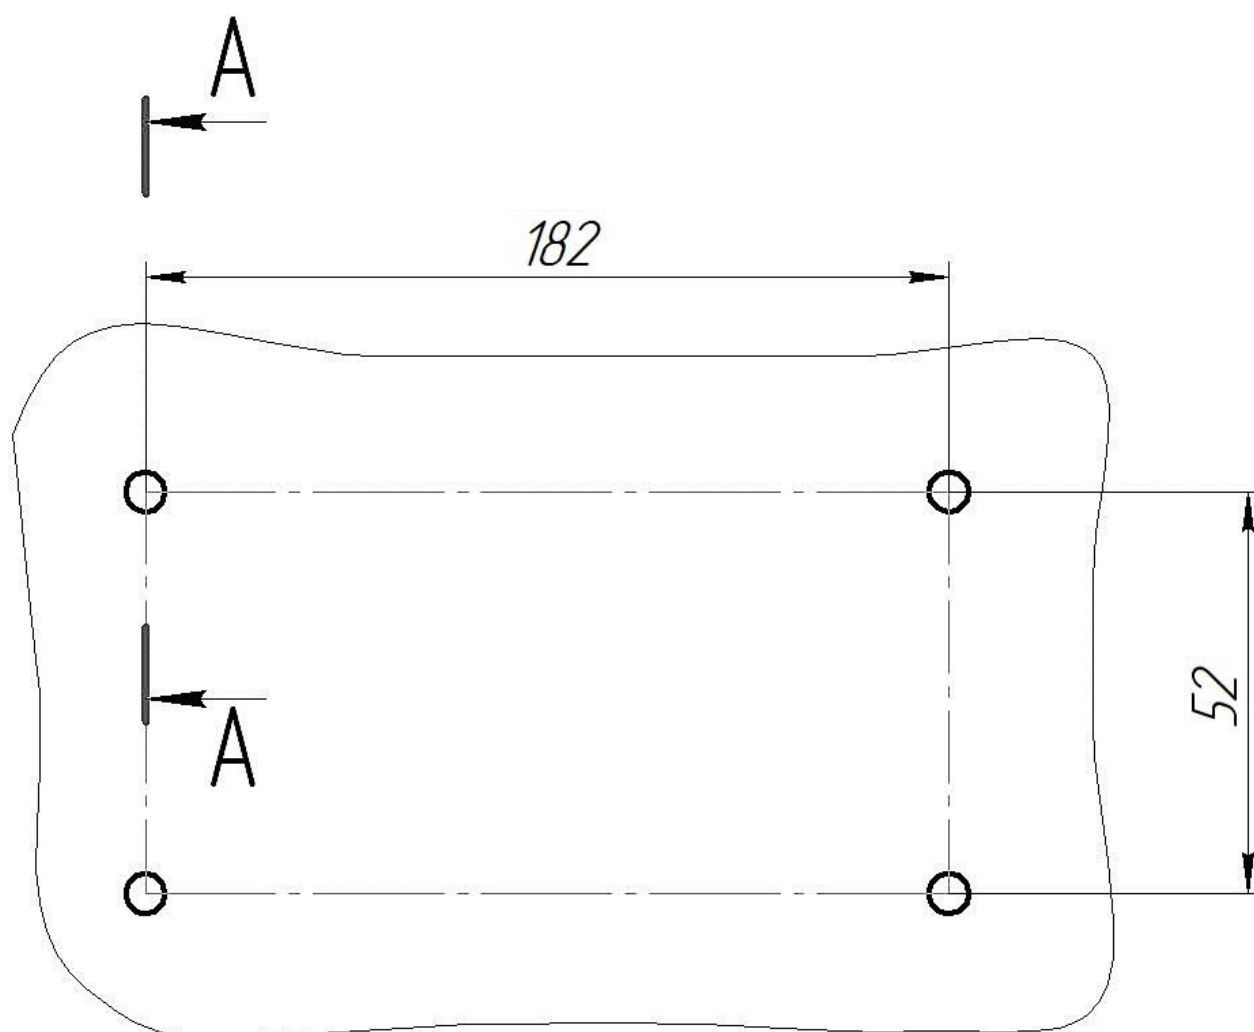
Разметка отверстий для крепления основного блока ПУИ-8
